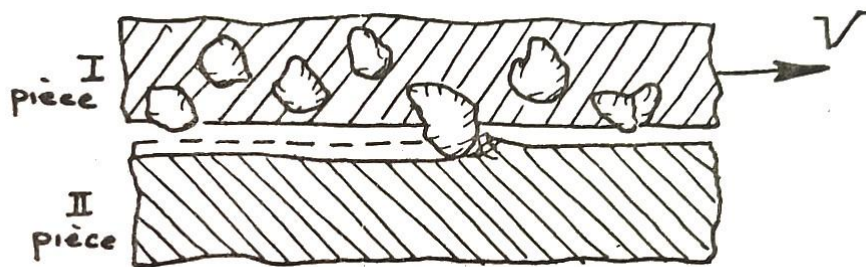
la destruction des surfaces de contact de deux pièces par les particules dures du métal de l'une des deux pièces
